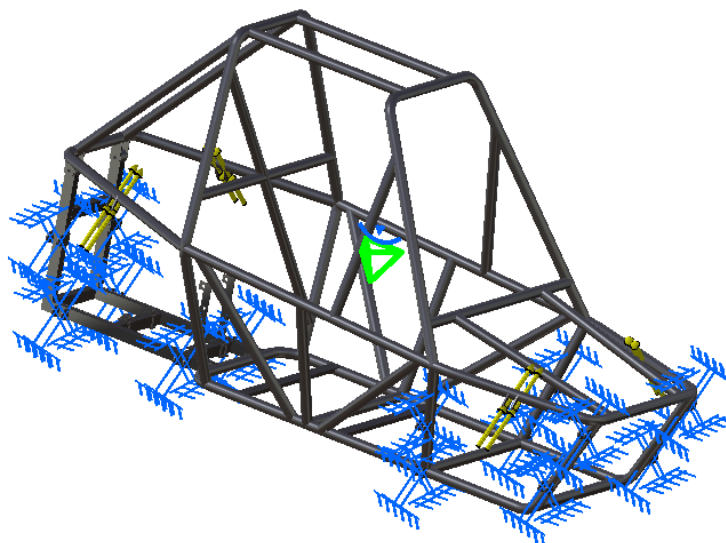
Fixação e aplicação de carregamento da estrutura para análise harmônica.
